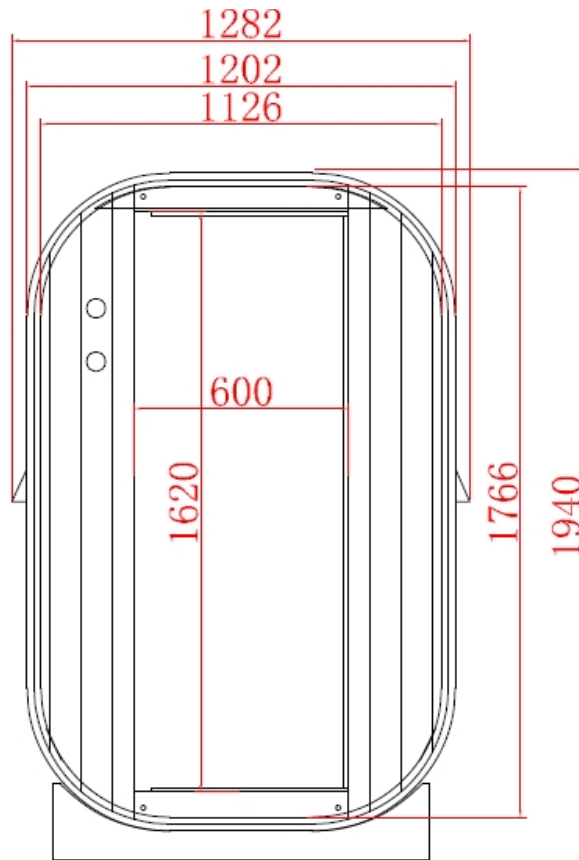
Croquis du Cube S, vue de face avec dimensions en mm
